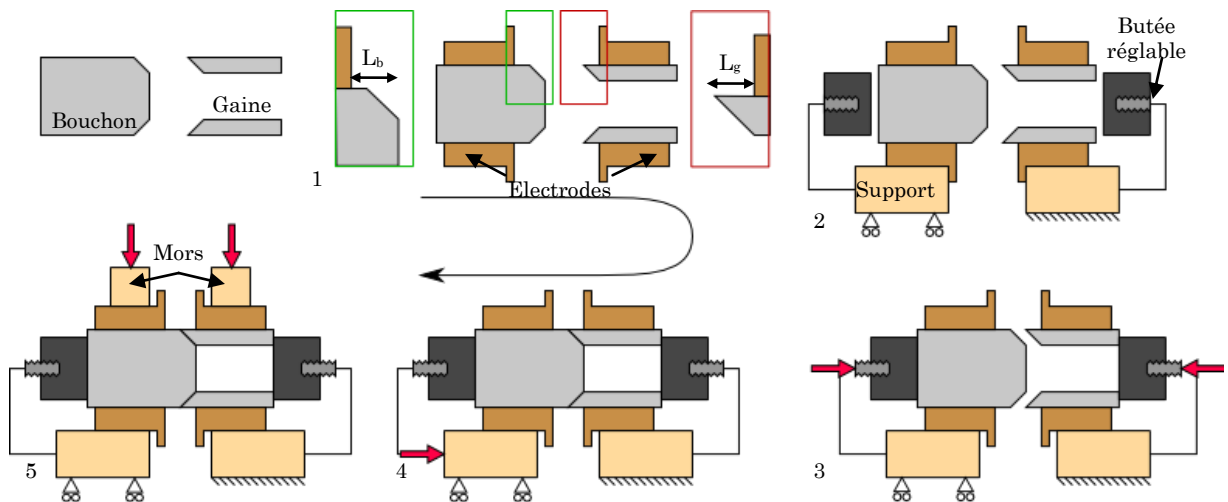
Protocole de mise en place des pièces dans les électrodes et sur la tête de soudage
